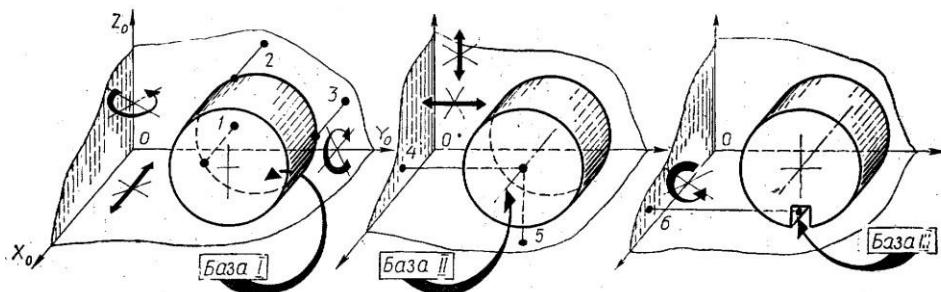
Базування короткого циліндричного тіла [3]
